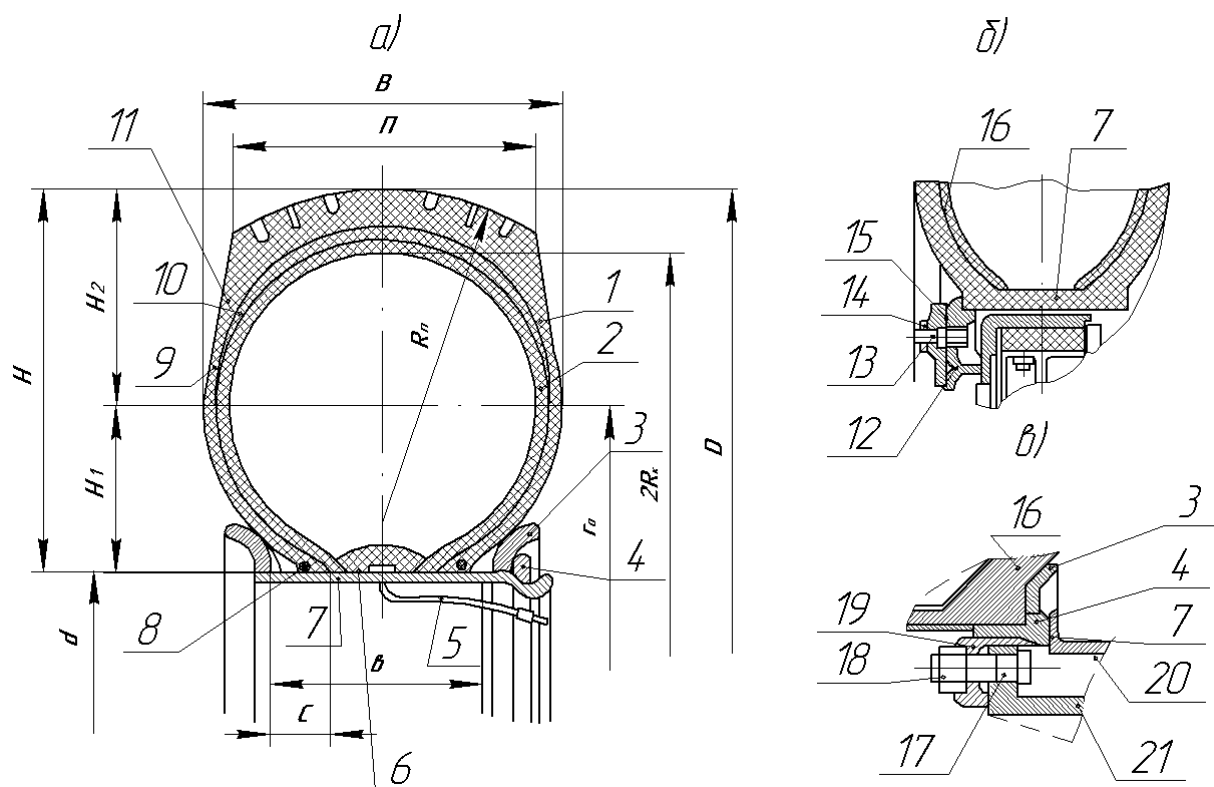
Конструктивні елементи бездискового пневматичного колеса тролейбусів ЗіУ–9: а – пневматична шина; б – кріплення одиночного (керованого) колеса; в – кріплення здвоєного (ведучого) колеса
